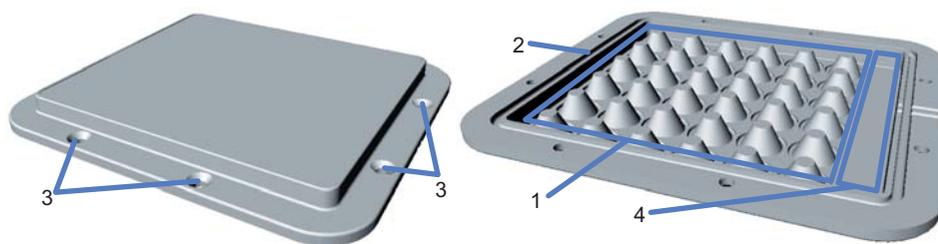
Конструкция мультилинзы NEMA: а) вид сверху; б) вид снизу. Цифрами обозначены: 1 — оптический блок линз; 2 — углубление для IP-уплотнителя; 3 — крепежные отверстия; 4 — пространство для установки разъема
